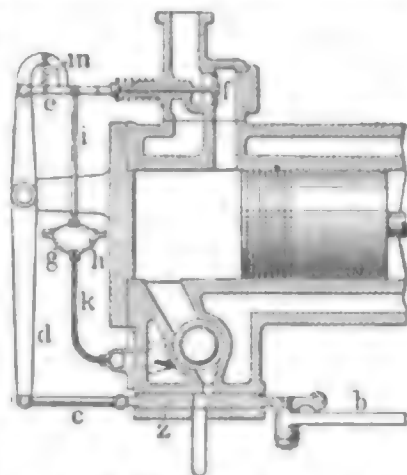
Steuerung der Gasmotorenfabrik Deutz.
